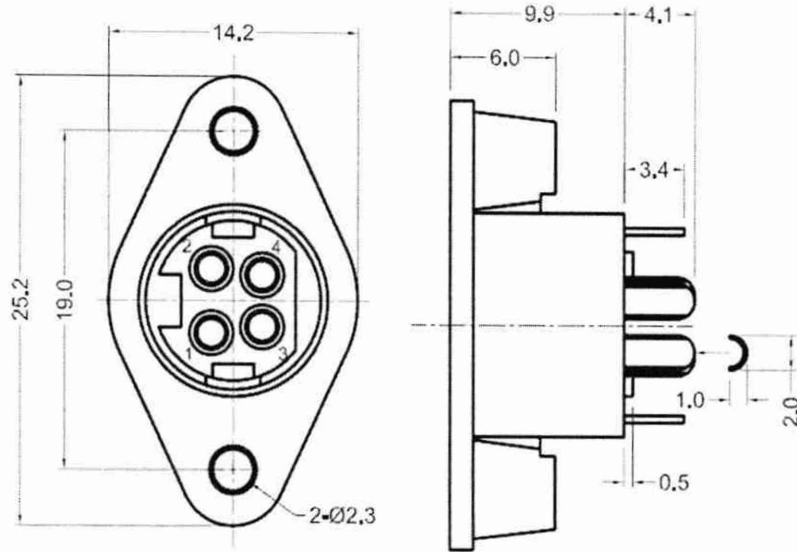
Внешний вид соединителя питания POWER розетка блочная KPJX-PM-4S (изготовитель KYCON)
